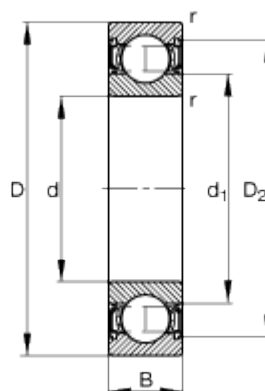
Rodamiento Rígido de Bola 6205(Sinfín)
